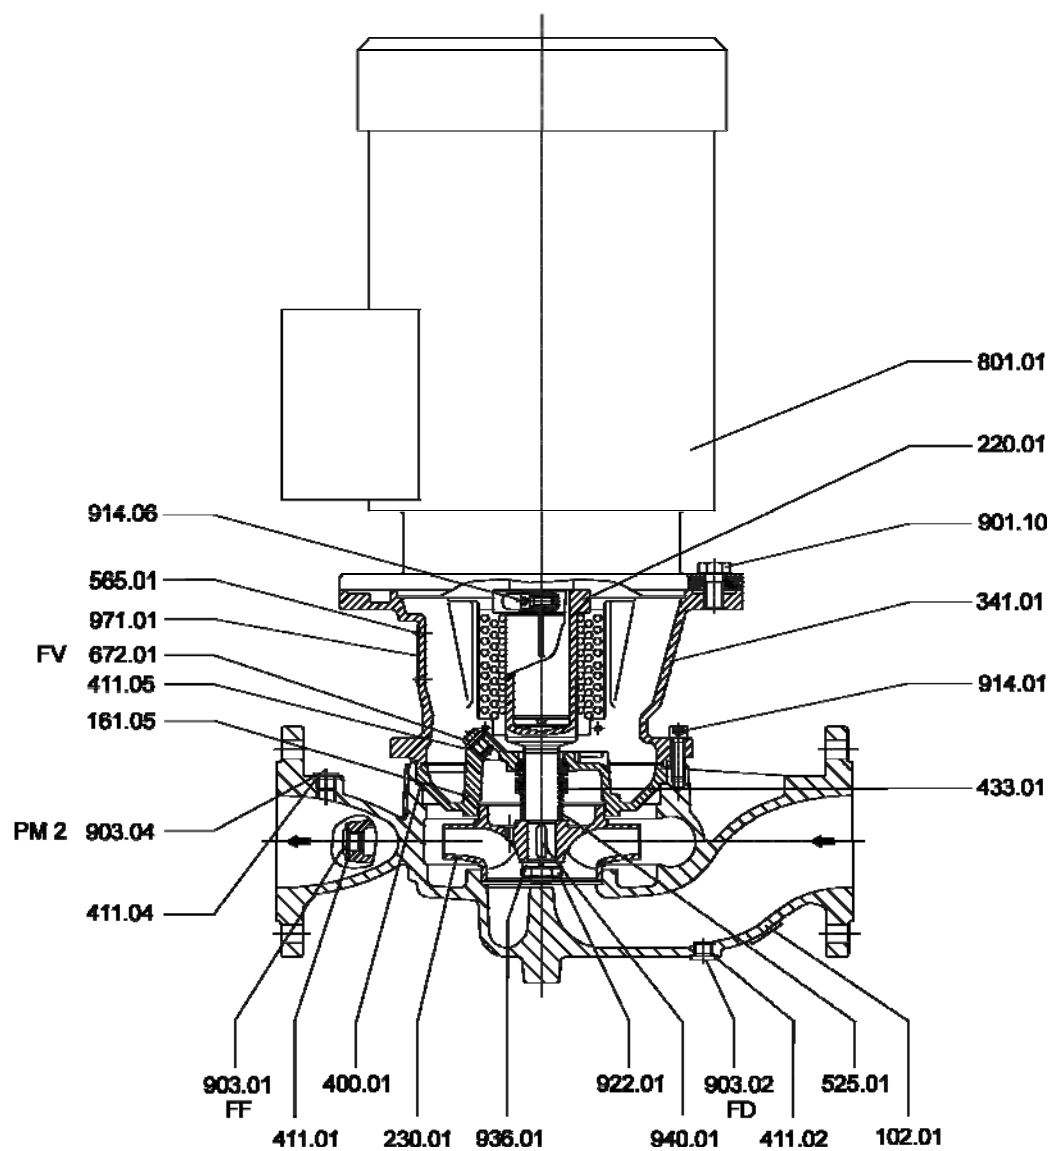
U3...D – Торцевое уплотнение под нагрузкой - типоразмер с диаметром 24 и 30 на уплотнении вала
